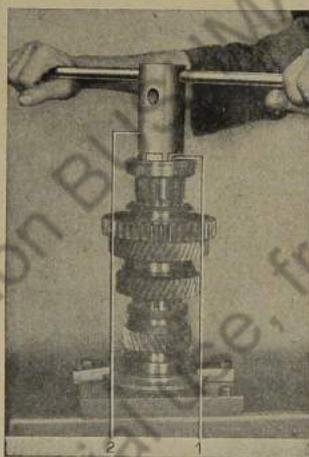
Nutmutter auf Hauptwelle aufschrauben
